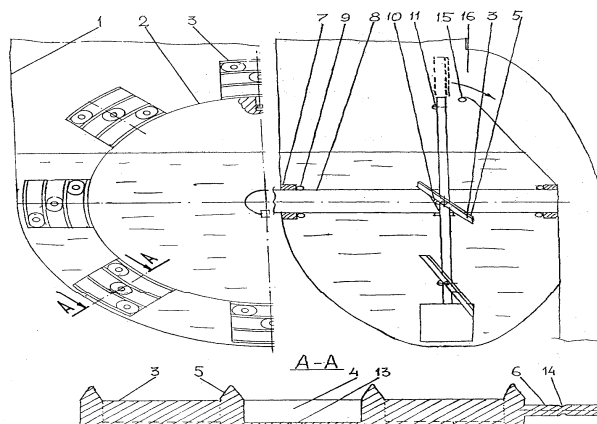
Высевающий аппарат с поворотными лопатками
